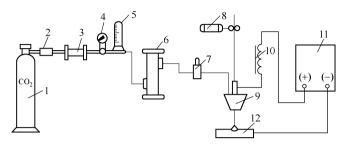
CO₂ 气体保护焊焊接设备组成示意图 1—CO₂ 气瓶 2—预热器 3—高压干燥器 4—气体减压阀 5—气体流量计 6—低压干燥器 7—气阀 8—送丝机构 9—焊枪 10—可调电感 11—焊接电源 12—工件
